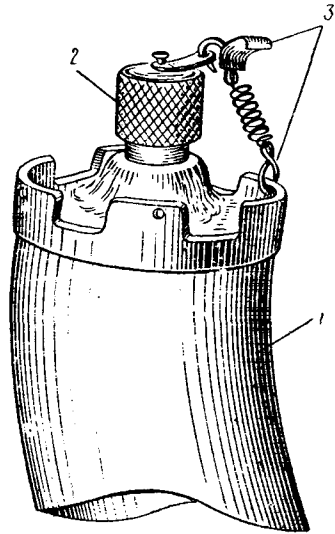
Контровка крышки заливной горловины маслосистемы редуктора и мерной линейки.
